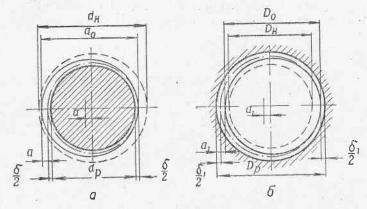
Определение нормализованных ремонтных размеров: а — для вала; б — для отверстий
